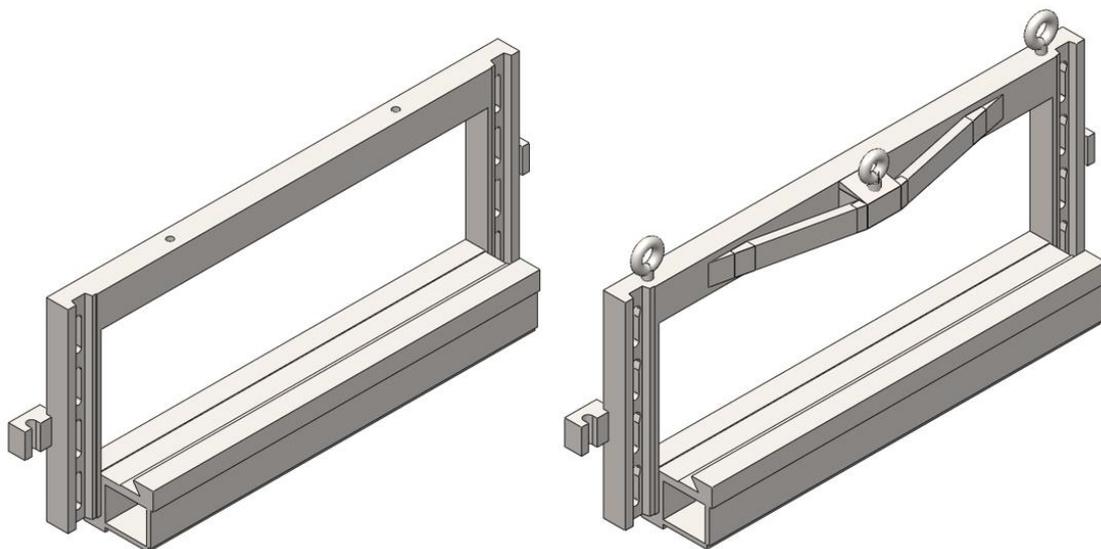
Desenho da proposta para alteração da estrutura das travessas.
